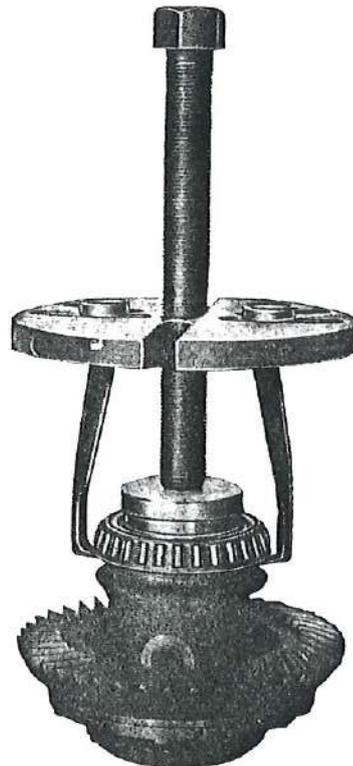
Desmontaje del anillo interior del rodamiento a rodillos mediante extractor A.6004 y las bridas A.40000.
